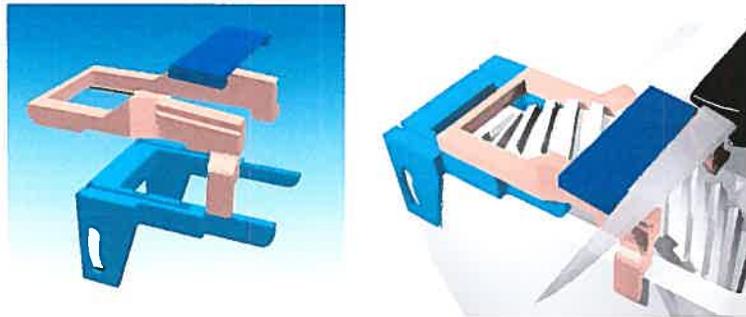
Explosive et assemblage du Quatrième modèle 3D¹⁵⁴
